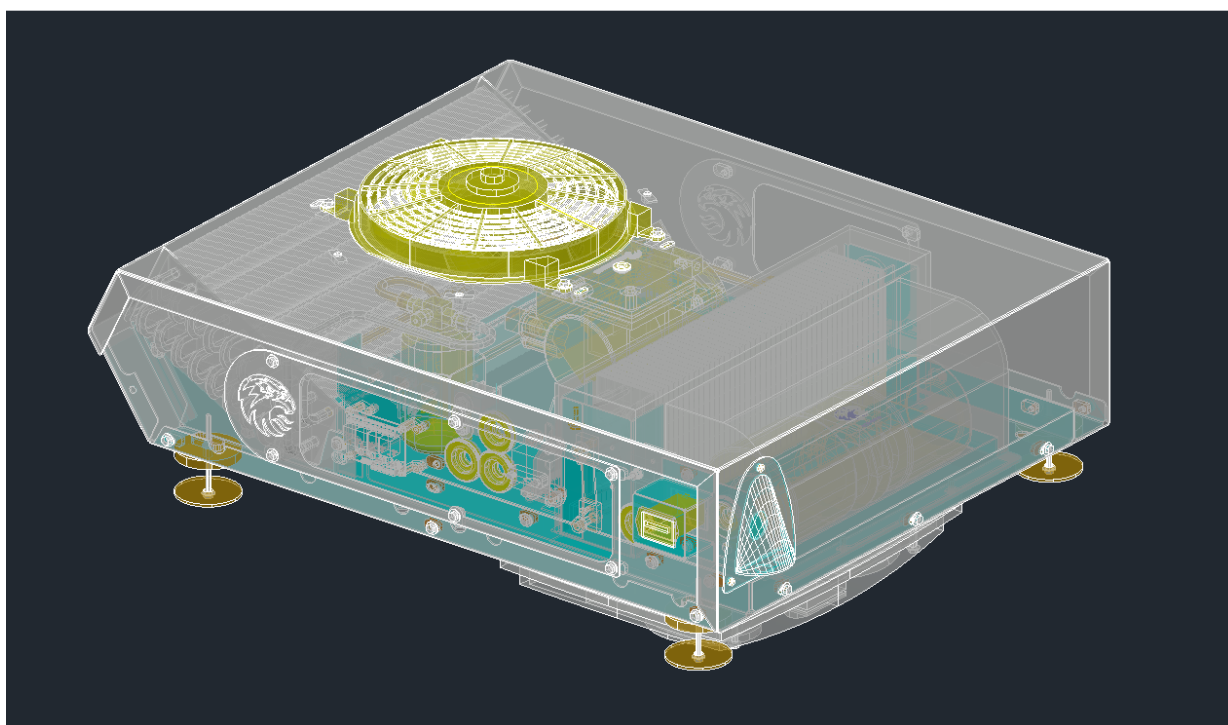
Unidad de Aire Acondicionado Serie AA-101-EC - Vista Isométrica
